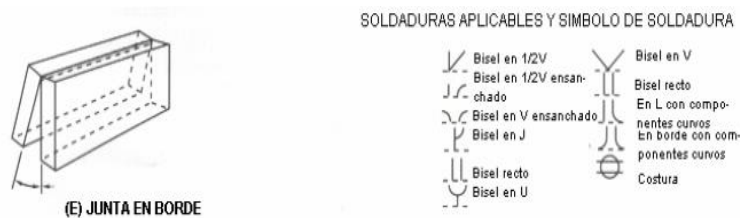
Junta en Borde y la soldadura aplicable.
